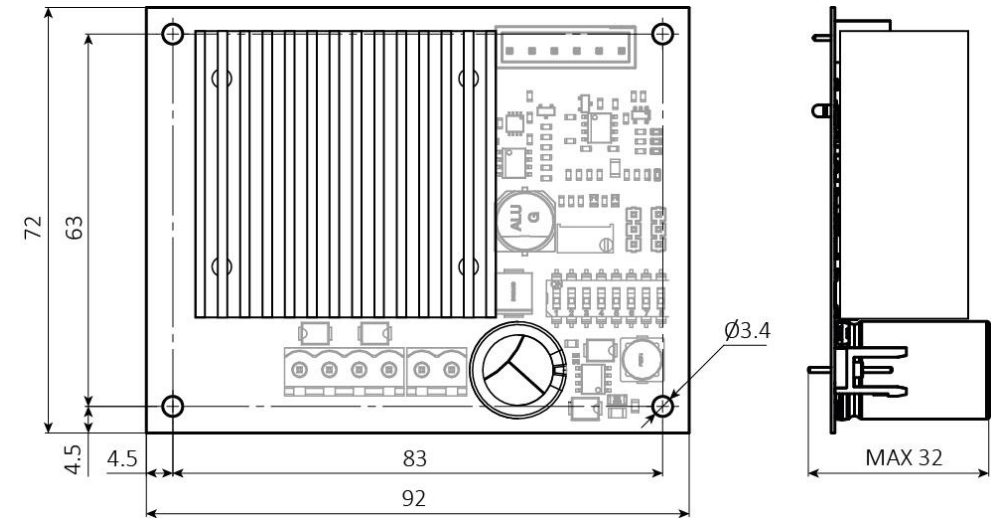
Габаритные и присоединительные размеры драйвера шагового двигателя SMD-2.8.
